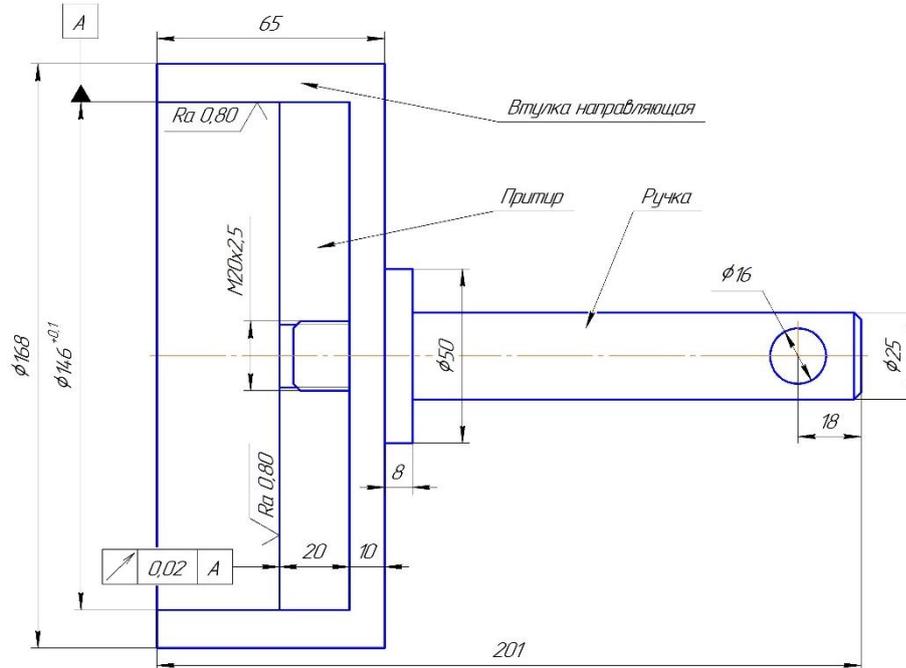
Притир для труби А622J.304129.004.001.001
